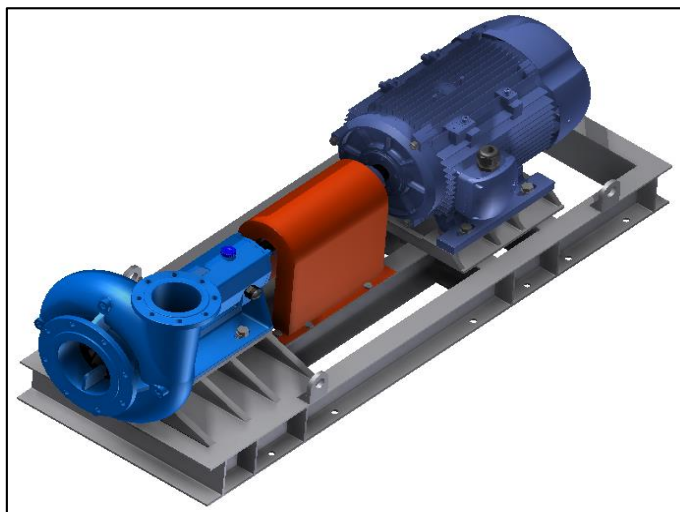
22 Placa base con marco de vigas estructurales con equipo de bombeo
